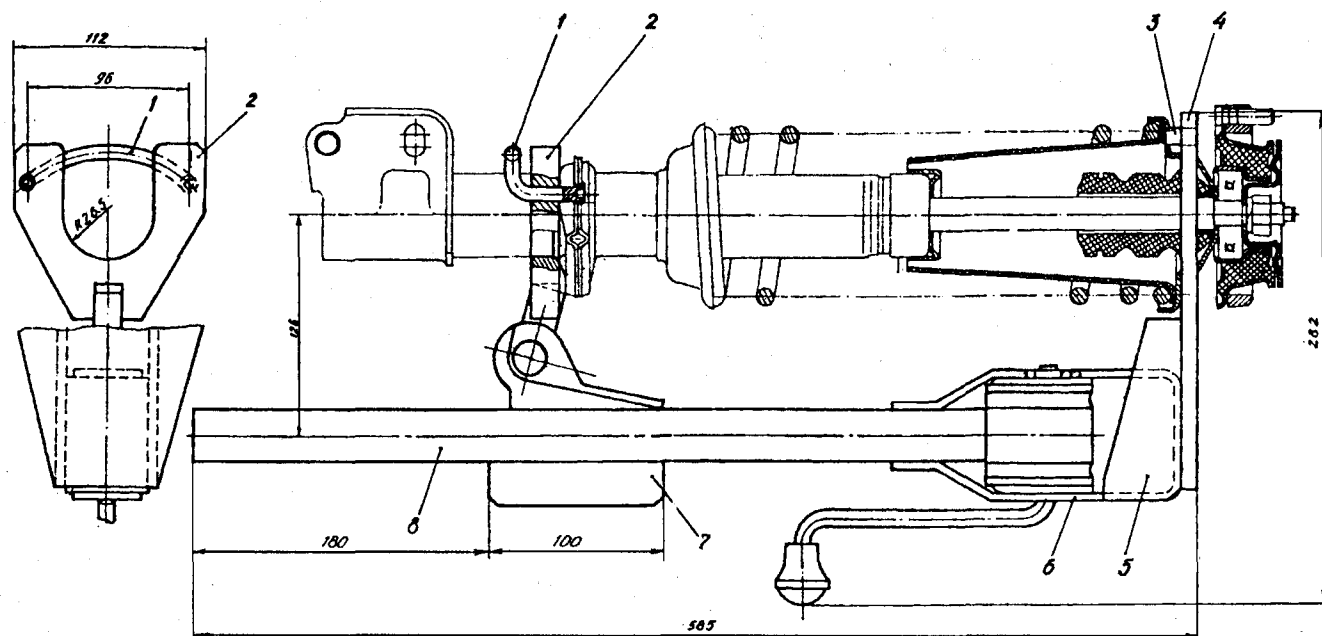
Приспособление для сборки и разборки пружины со стойкой передней подвески: 1 – скоба; 2 – вилка; 3 – упор; 4 – захват; 5 – косынка 6 – стремянка; 7 – фланец; 8 – приводной механизм
